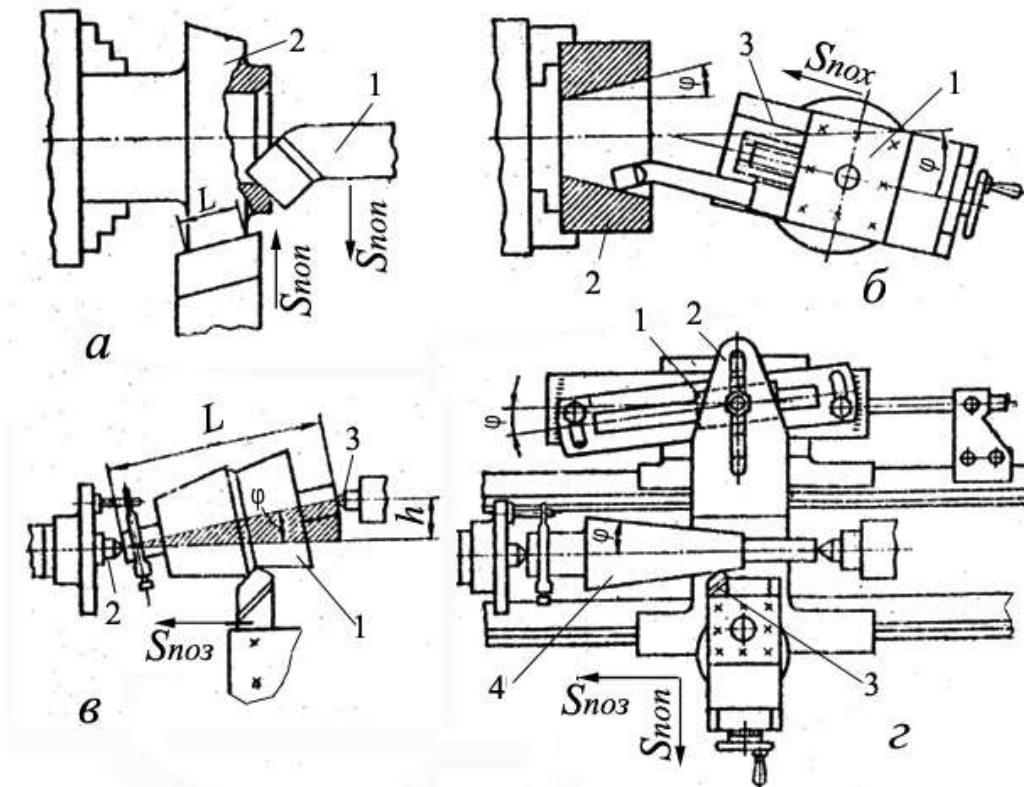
Обробка конічних поверхонь на токарному верстаті
